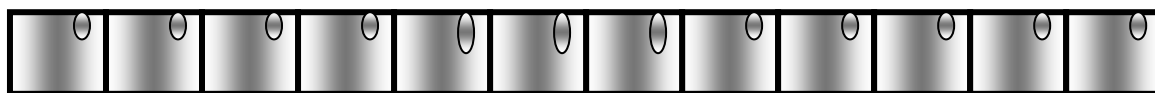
Схема контактных пятен зубьев ведущей шестерни редуктора
